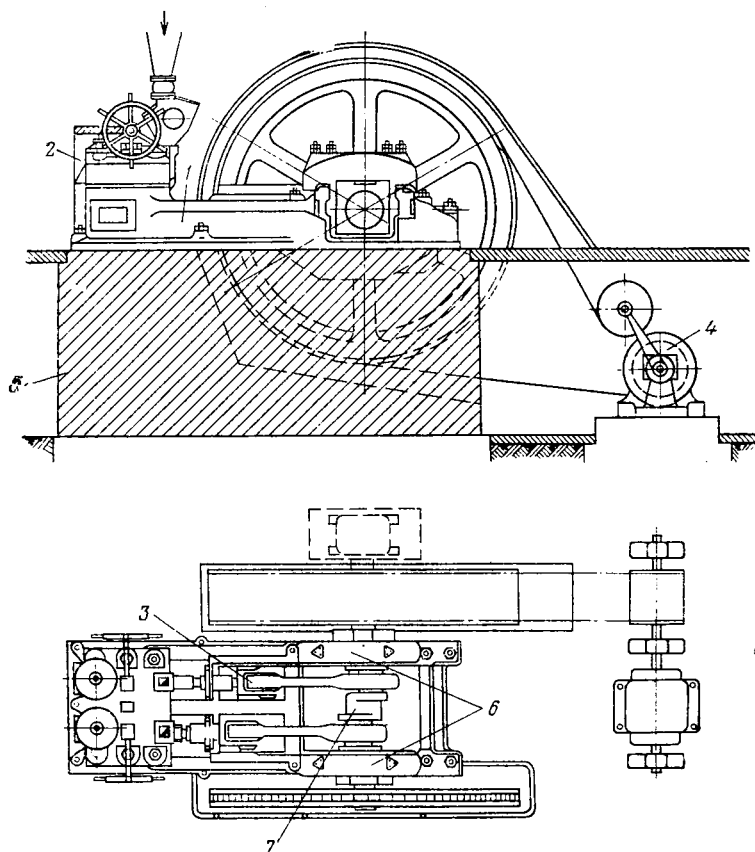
Двухштемпельный кривошипно-шатунный пресс
